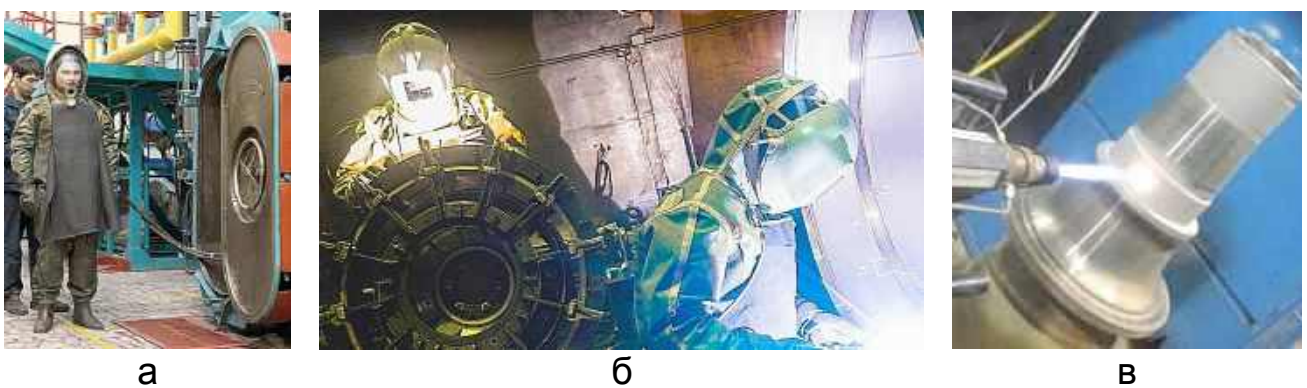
Аргоно-дугове зварювання титанових конструкцій у шлюзовій камері: а – зварник у скафандрі; б – загальний вигляд робочих місць зварників у шлюзовій камері; в – процес приварювання маточини до стояка шасі літака
